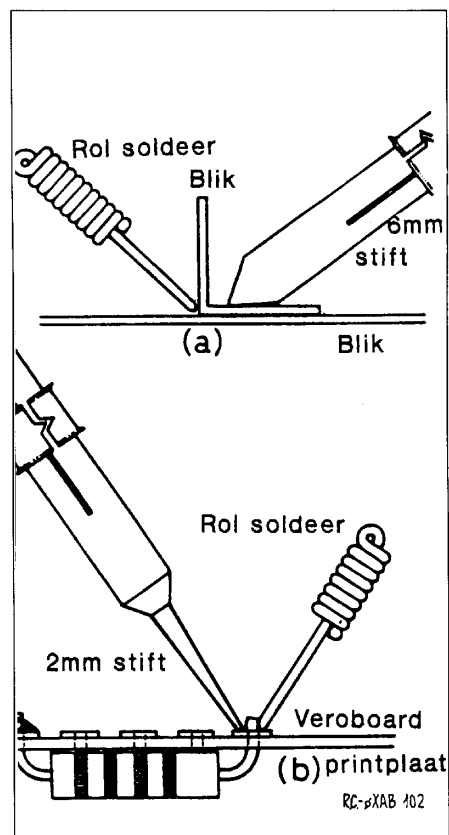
Gebruik een flinke soldeerstift (a) voor het solderen van blik en een dunne stift (b) voor de componenten. Let op de handige vorm van de rol soldeer.
